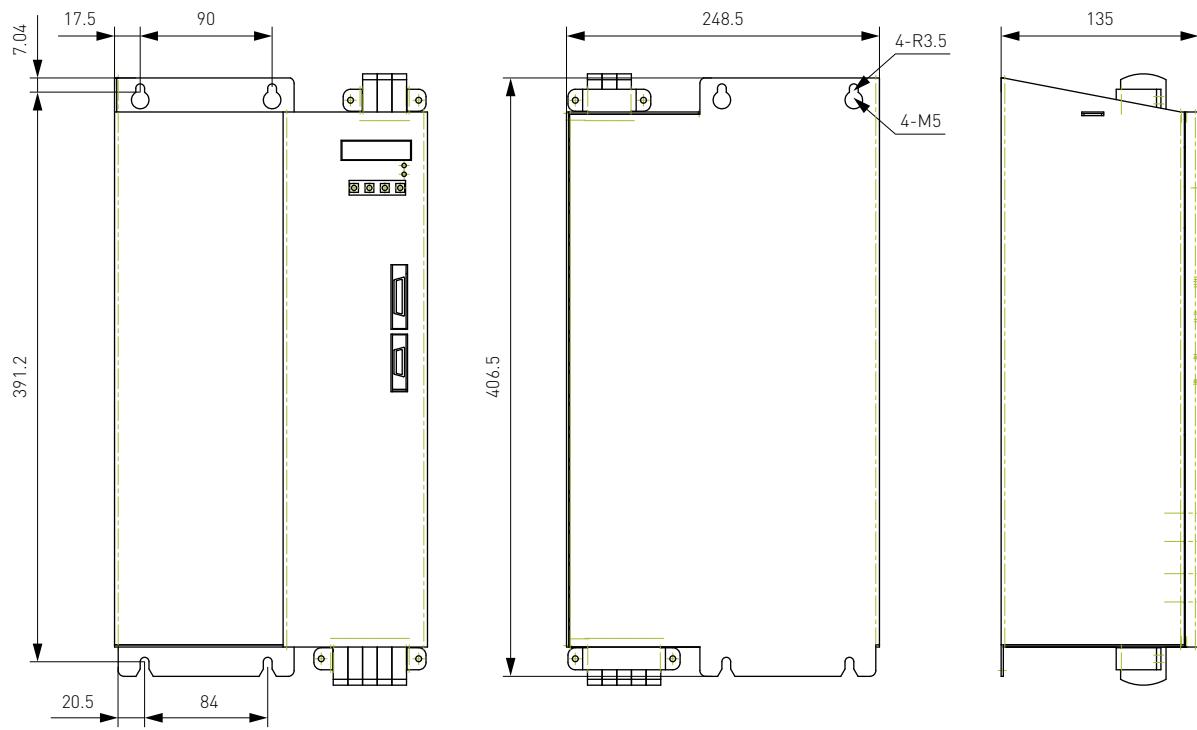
Габаритный чертеж серводрайверов А7-18.5KW, А7-22KW, А7-30KW.
